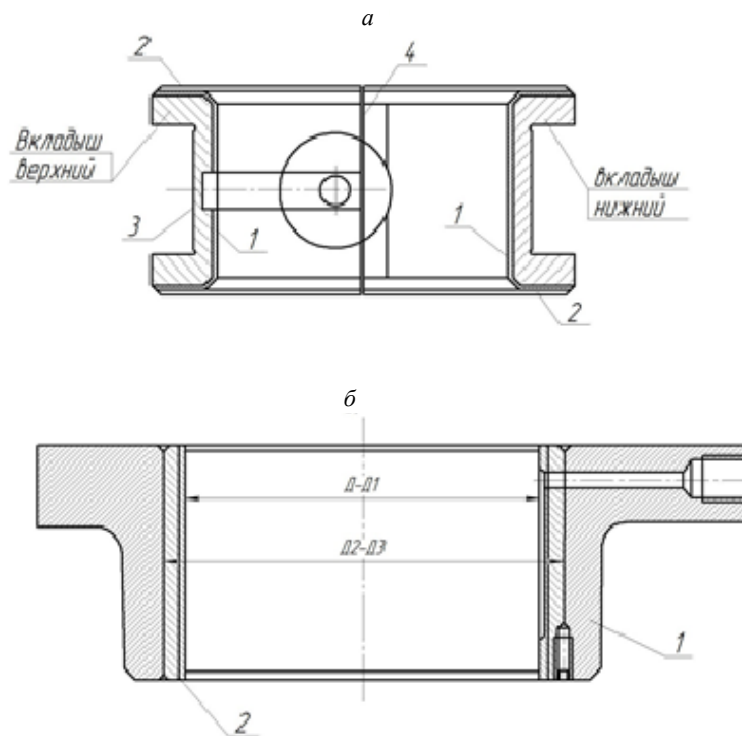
Конструкции: а – вкладыша упорного подшипника (1, 2 – антифрикционный слой, 3 – корпус подшипника); б – подшипника опорного концевое (1 – корпус подшипника, 2 – антифрикционный слой)
